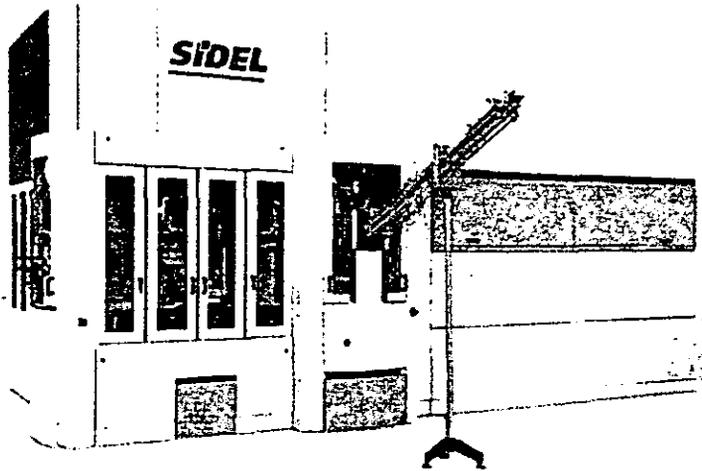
Vista general de una máquina sopladora SIDEL SBO20
